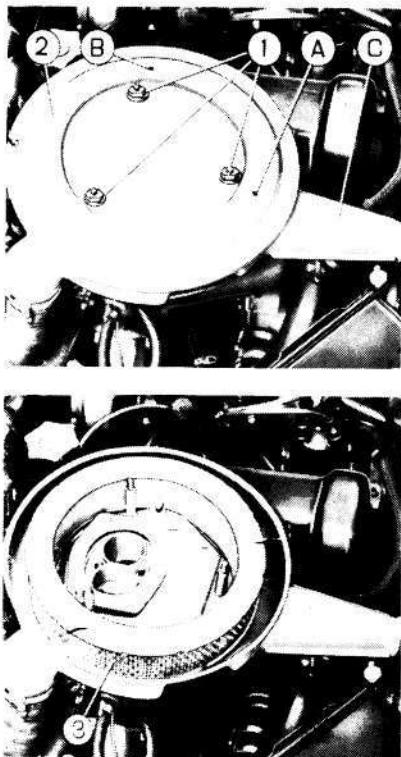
Воздушный фильтр: 1 — гайки; 2 — крышка фильтра; 3 — фильтрующий элемент
